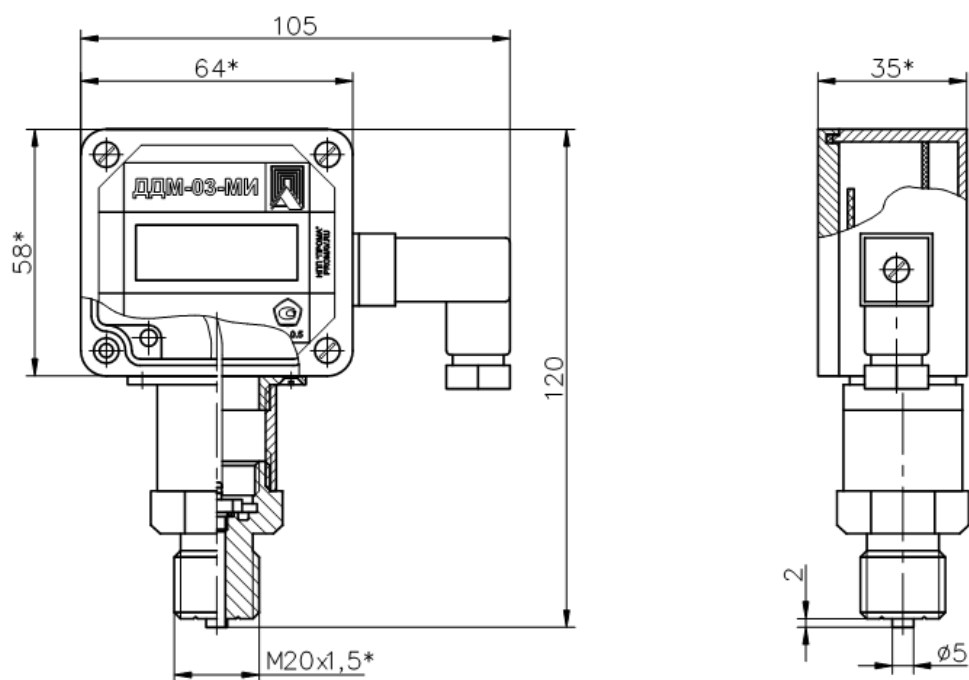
Габаритные и присоединительные размеры датчика ДДМ-03-ДИ (ДВ, ДИВ, ДА)-МИ-03 с индикатором.
